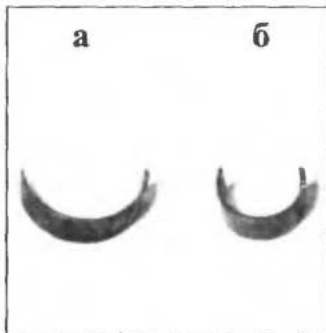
Заготовка вкладыша до (а) и после (б) гибки
